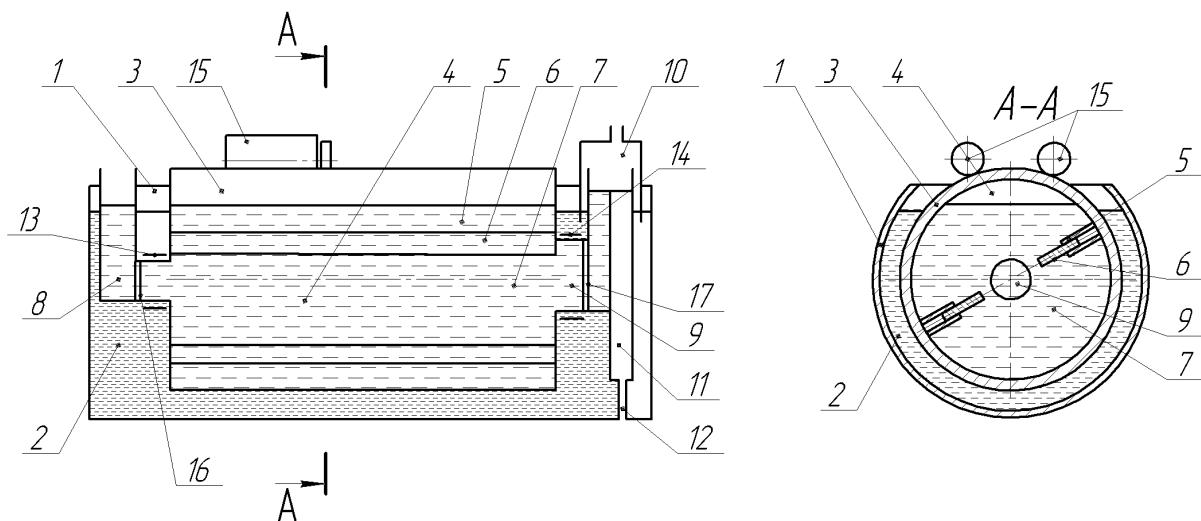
Схема біогазового обертового реактора, модульного типу: 1 – горизонтальний зовнішній корпус; 2 – рідина; 3 – циліндричний реактор; 4 – камера зброджування; 5 – перегородка; 6 – рухомі пластини; 7 – органічна маса; 8, 9, 12 – патрубки; 11 – вивантажувальна камера; 13, 14 – підшипникові вузли; 15 – зовнішній привод; 16, 17 – блок-ущільнення.
